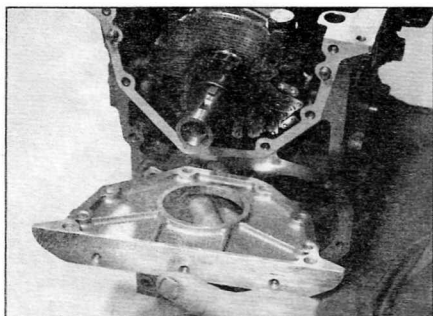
Снятие корпуса манжеты с блока цилиндров
